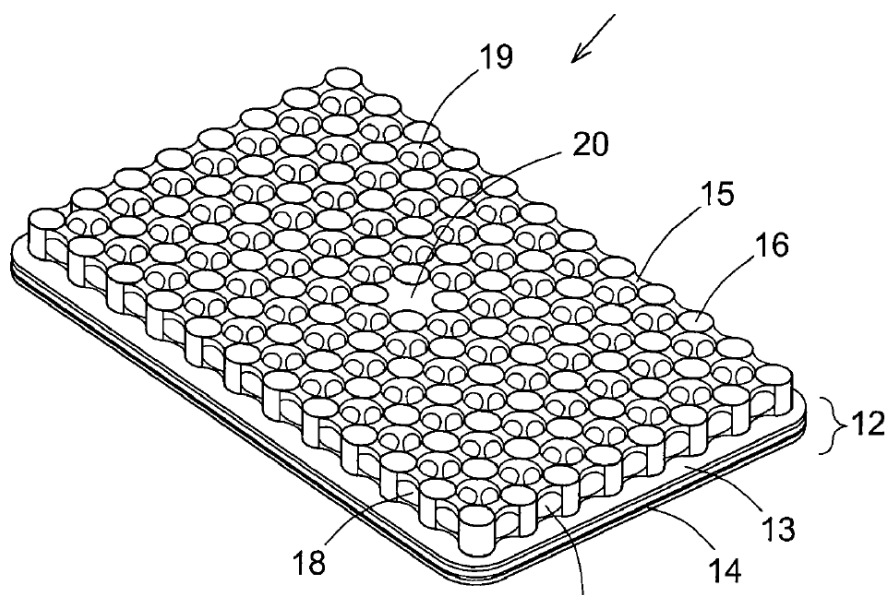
Облегчённый держатель для пробирок [124]
